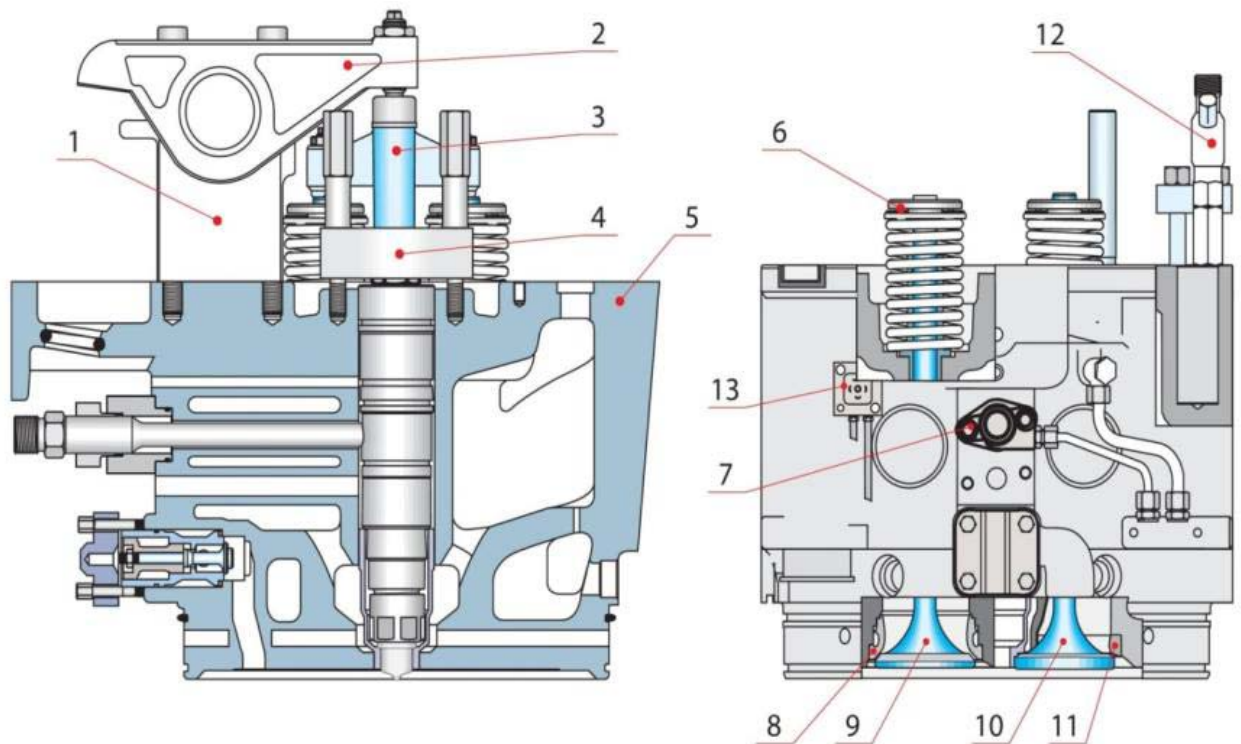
Головка блоку циліндрів: 1 – опірна стійка; 2 – коромисло; 3 – траверса для клапанів; 4 – траверса для форсунки; 5 – корпус головки; 6 – обертаючий пристрій; 7 – гвинти; 8 – сидло випускного клапана; 9 – випускний клапан; 10 – впускний клапан; 11 – сидло впускного клапана; 12 – індикаторний кран; 13 – датчик температури
